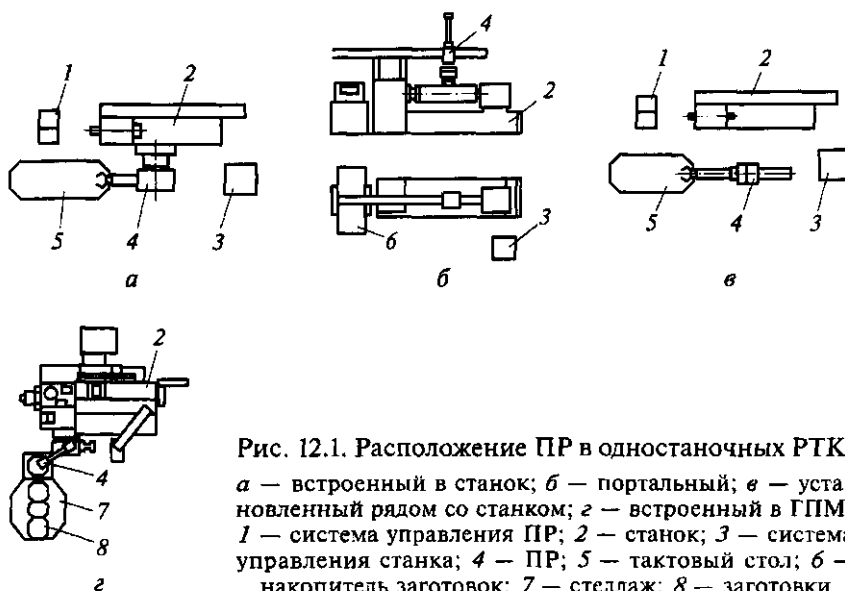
Расположение ПР в одностаночных РТК: *а* — встроенный в станок; *б* — порталный; *в* — установленный рядом со станком; *г* — встроенный в ГПМ; 1 — система управления ПР; 2 — станок; 3 — система управления станка; 4 — ПР; 5 — тактовый стол; 6 — накопитель заготовок; 7 — стеллаж; 8 — заготовки
